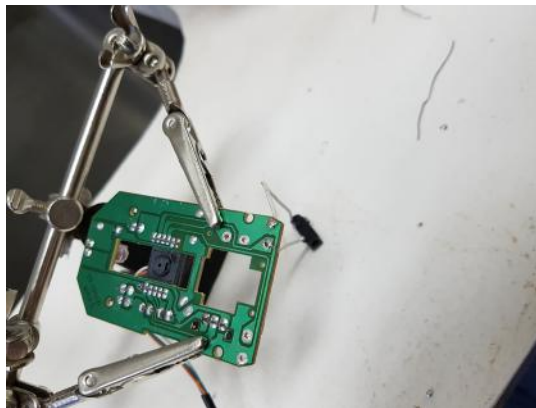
Plugue P2 fêmea soldado na PCB
